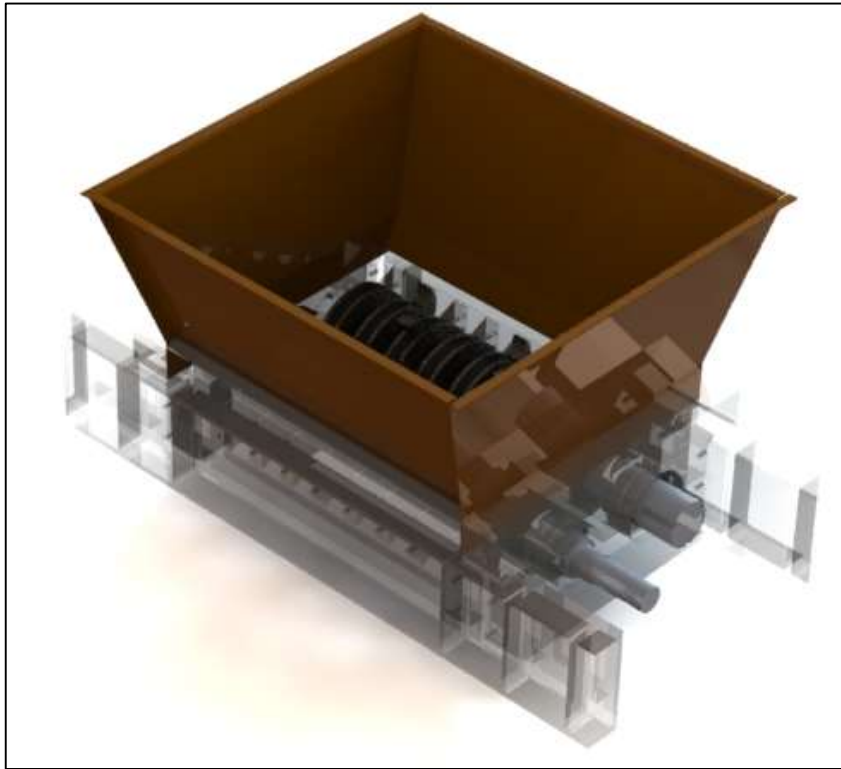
Vista frontal del diseño de la tolva de almacenaje.
